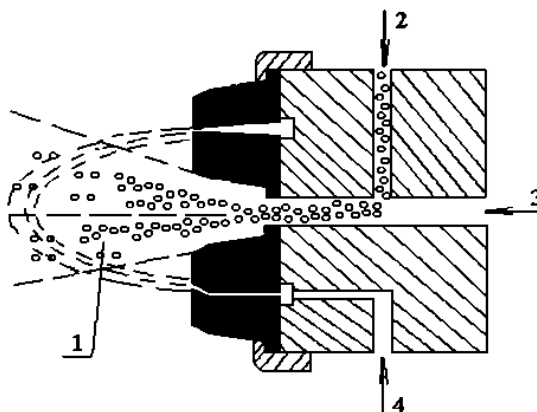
Эскиз процесса нанесения газопламенного покрытия из порошка: 1-газовое пламя; 2-подача порошка; 3-подача сжатого воздуха; 4-подача горючей смеси газов
